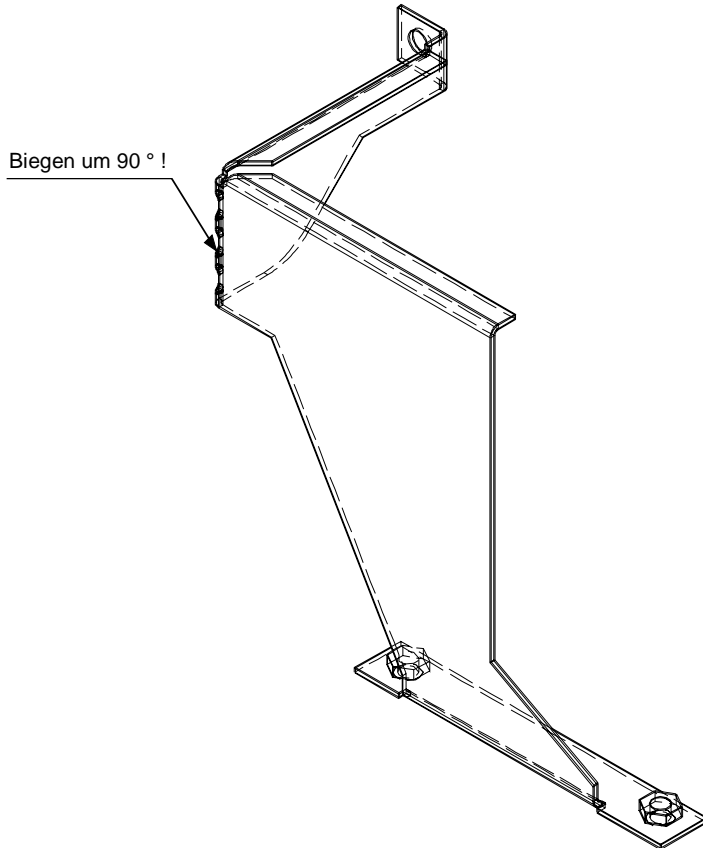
Endzustand des Haltebleches für die SSB-Baugruppe
